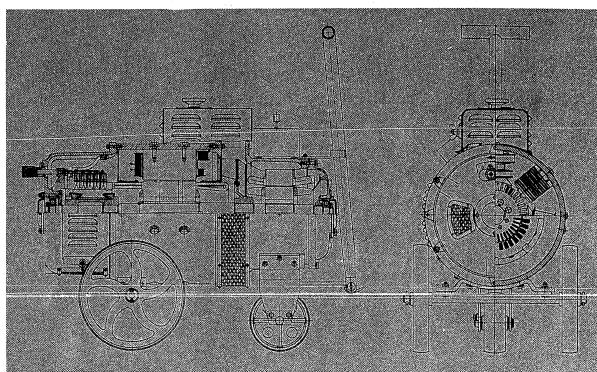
Общий вид (разрез) преобразователя типа ПС-300
